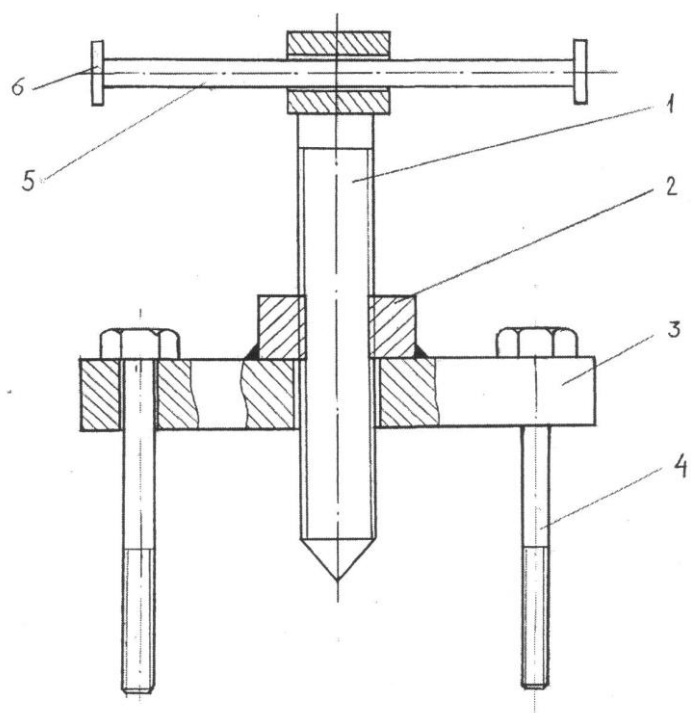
Пристрій для зняття передньої кришки генератора:
